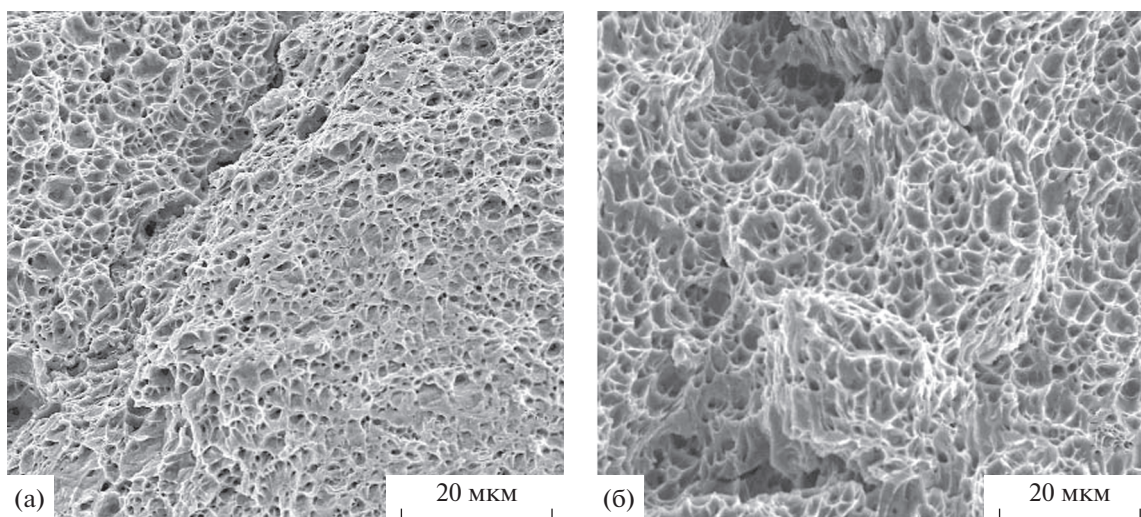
Фрактограммы образца сварного соединения с надрезом по линии сплавления шва ГДС: а – область зарождения трещины; б – область развития трещины.
